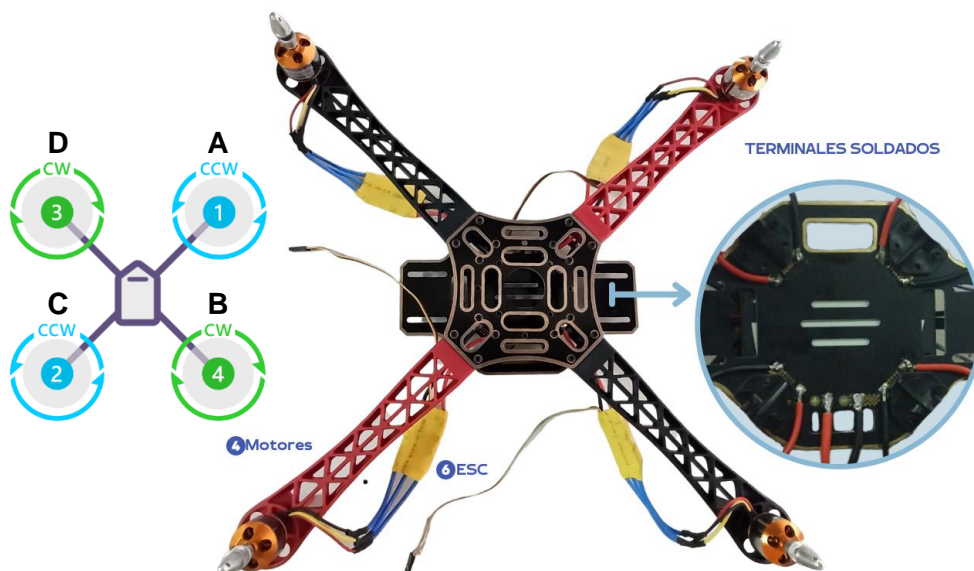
Ubicación y sentido de giro de motores & soldadura de ESCs [Fuente propia]
